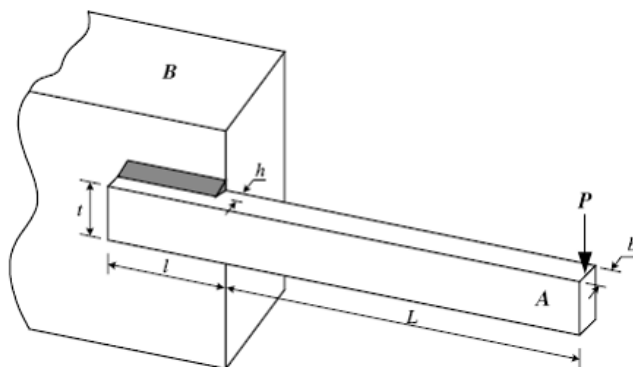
Схема сварной конструкции балки [9]
